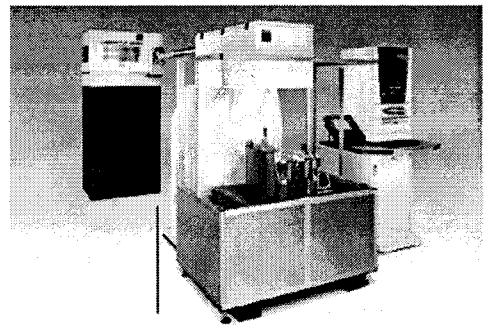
CO₂ 레이저 Remote welding system
